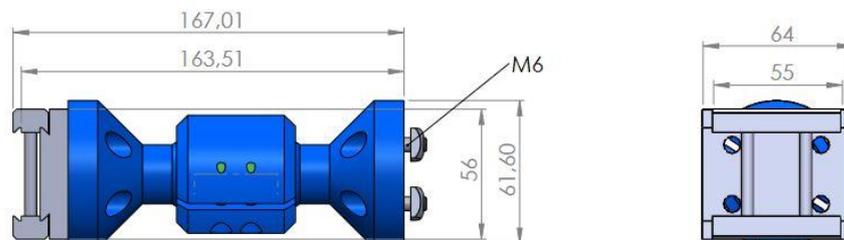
Montage-Kit – Technische Ansicht (Quelle: Autovimation)
